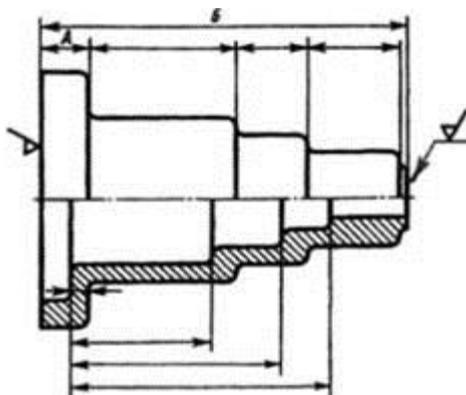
Нанесение наружных и внутренних размеров детали
